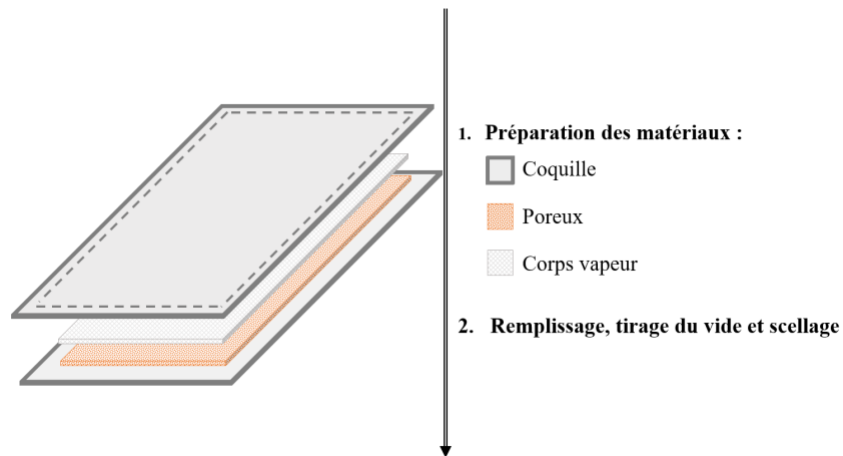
Procédé de fabrication/assemblage suggéré.
